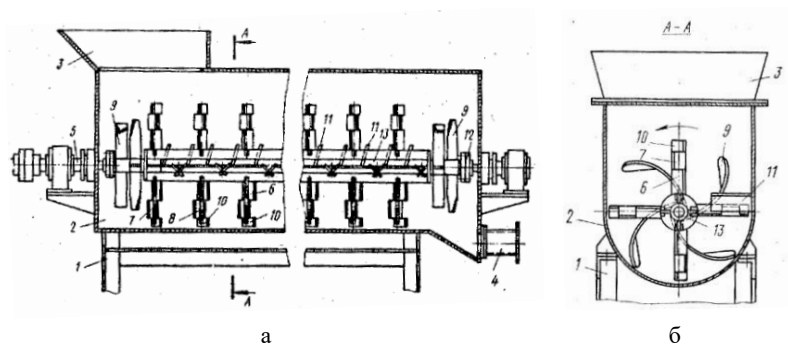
Конструкция лопастного смесителя: а-продольный разрез; б- сечение А-А.
